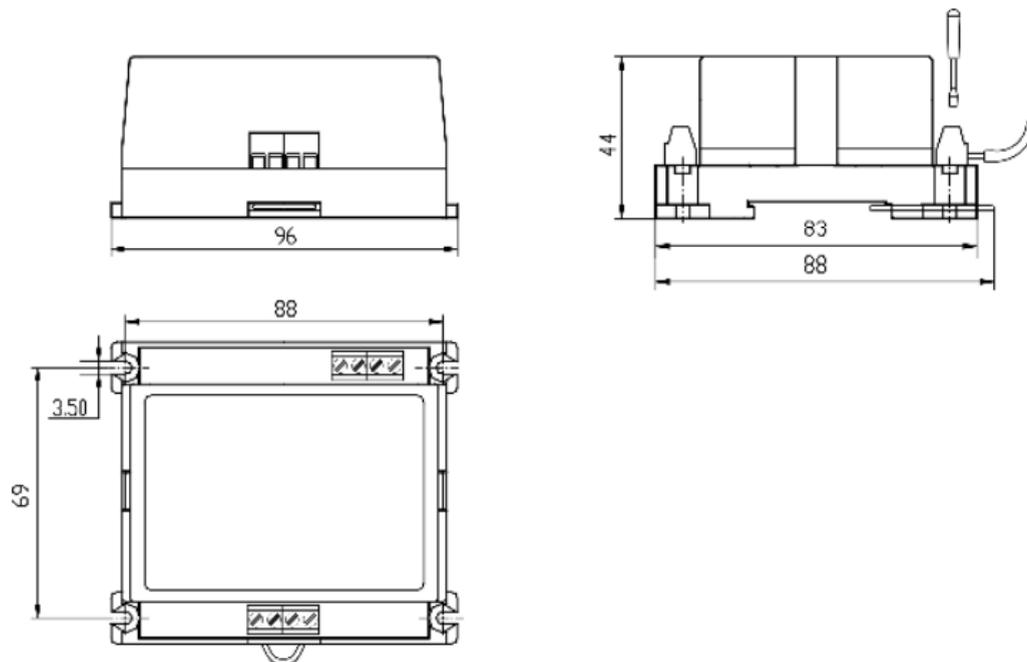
Габаритные и присоединительные размеры фильтра
